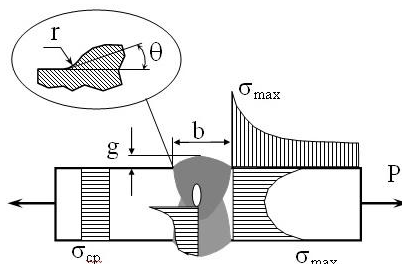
Распределение напряжений в зоне сопряжения основного и наплавленного металла, в вершине острых дефектов
